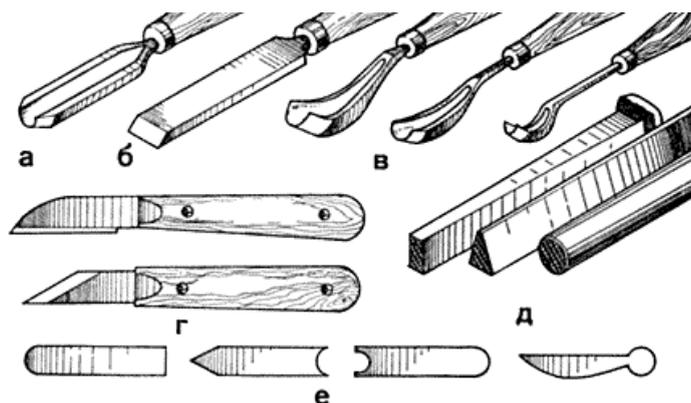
Основные инструменты для выполнения резьбы по гипсу:
